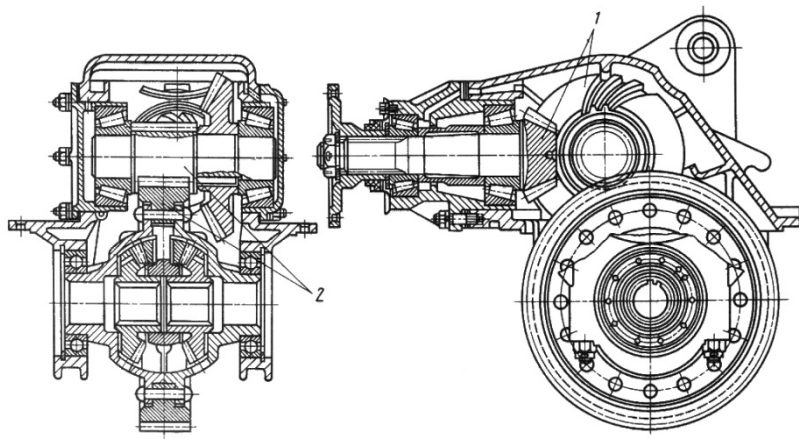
Двойная центральная главная передача со смещением ведомой цилиндрической шестерни вниз: 1 — коническая зубчатая пара; 2 — цилиндрическая зубчатая пара
